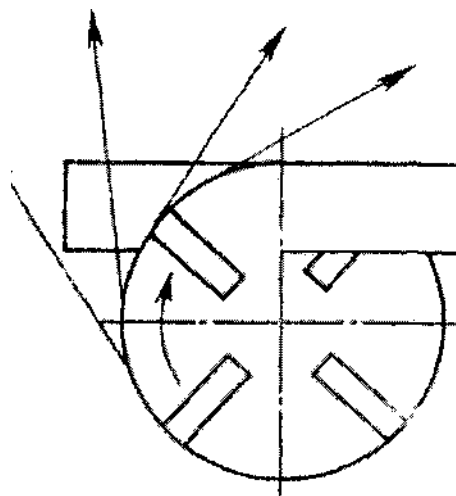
Пневмовідцентровий робочий орган (вид зверху).
